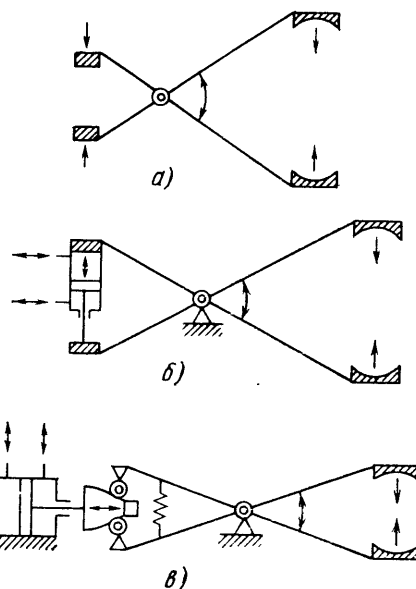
Схема кинематической пары вращения (а), захват с использованием кинематической пары вращения и цилиндра с поршнем (б), захват с использованием цилиндра с поршнем и кулачка (в)
